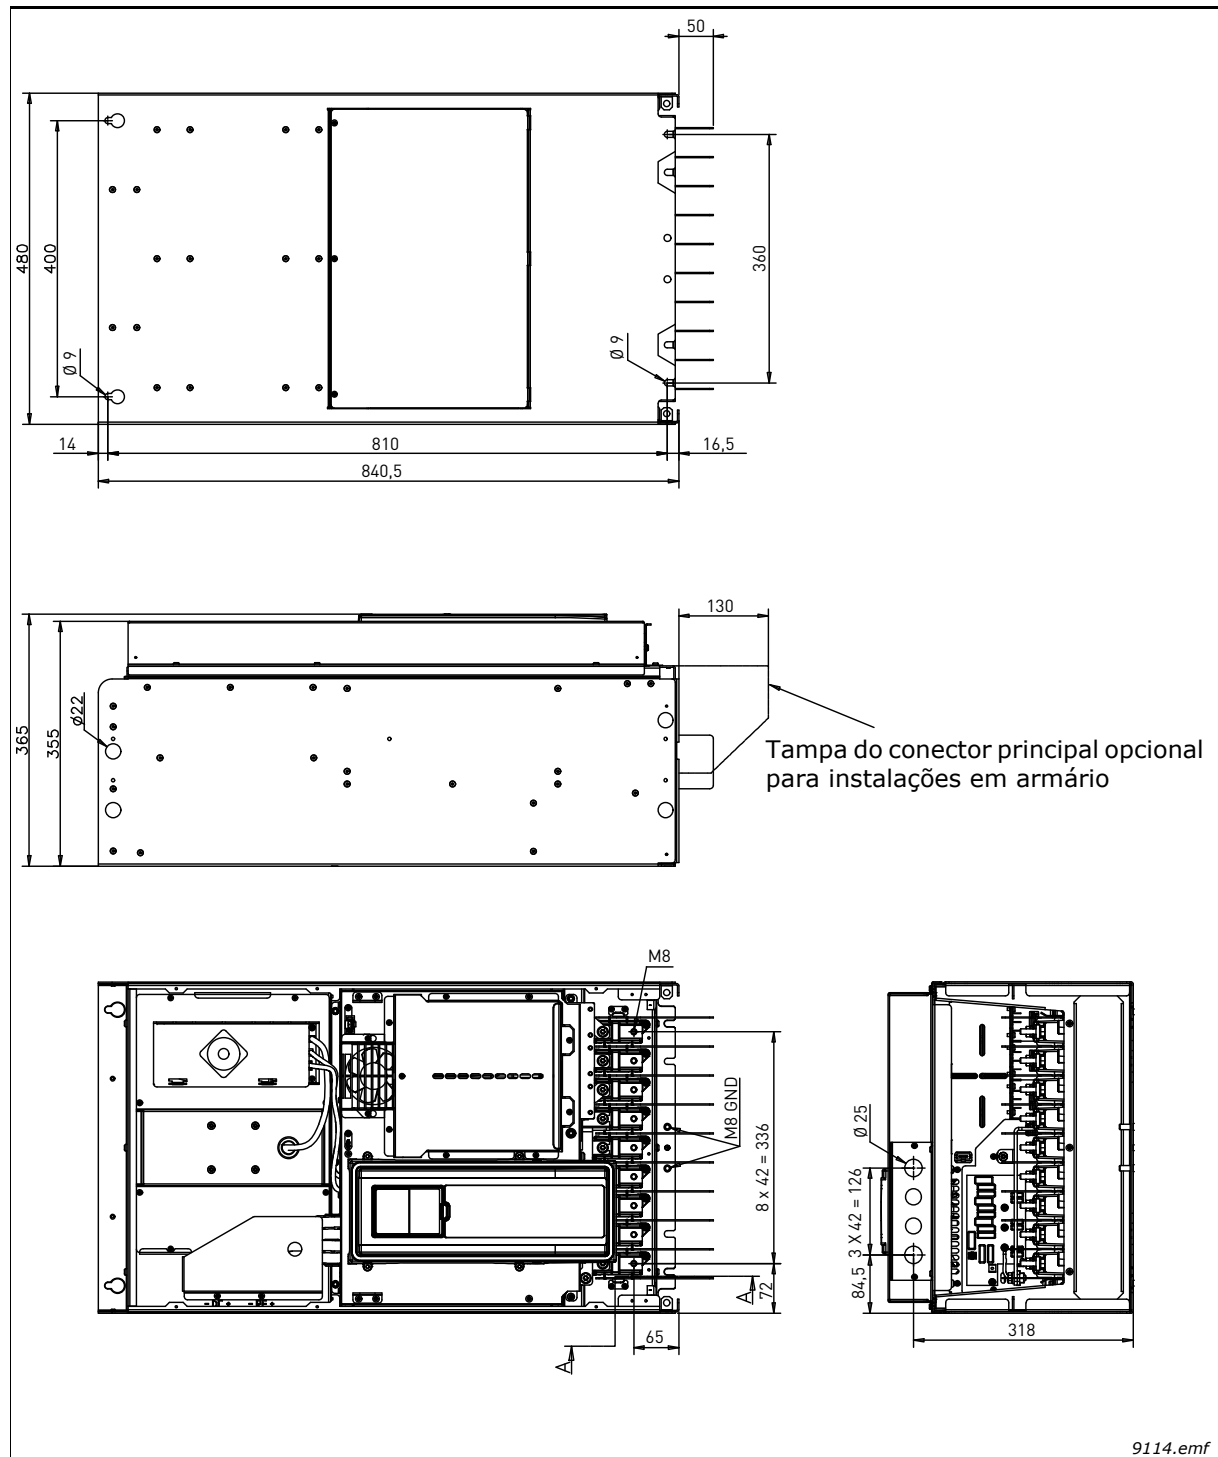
Dimensões do inversor de CA Vacon, MR9 IP00
